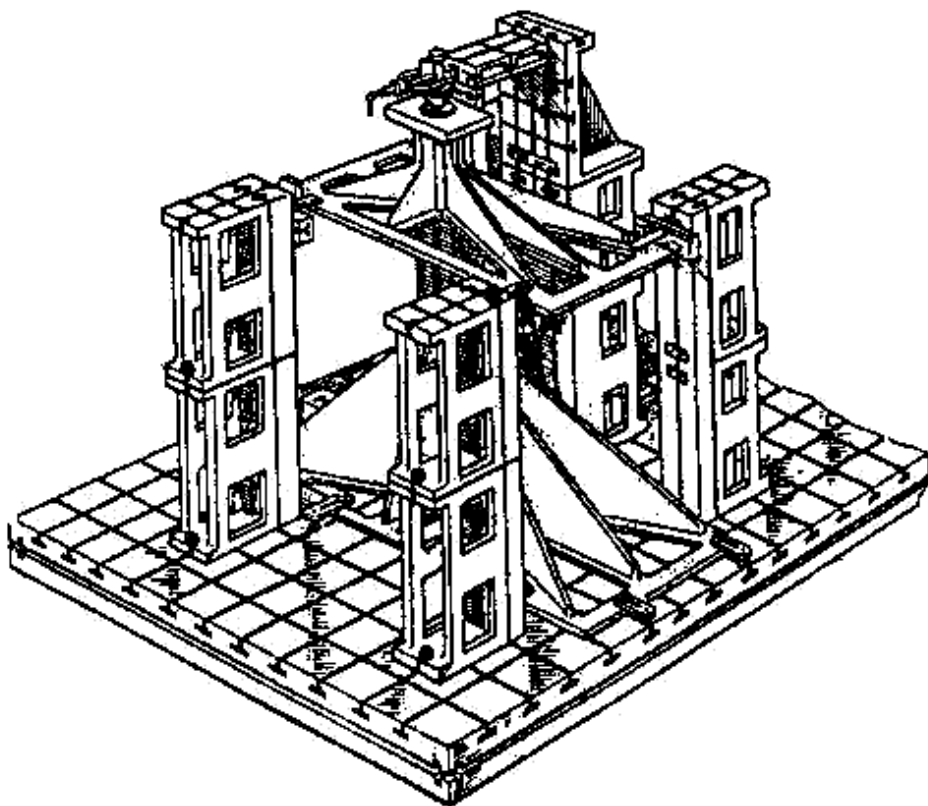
Приспособление для сборки и сварки крупных агрегатов
